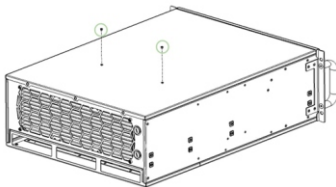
Извлечение винтов фиксации верхней крышки с корпусом
